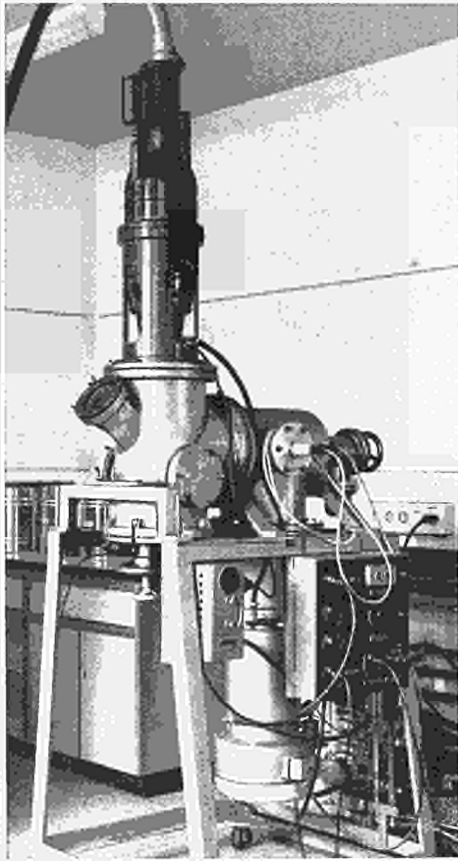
Elektronenstrahl-Schweißapparat
